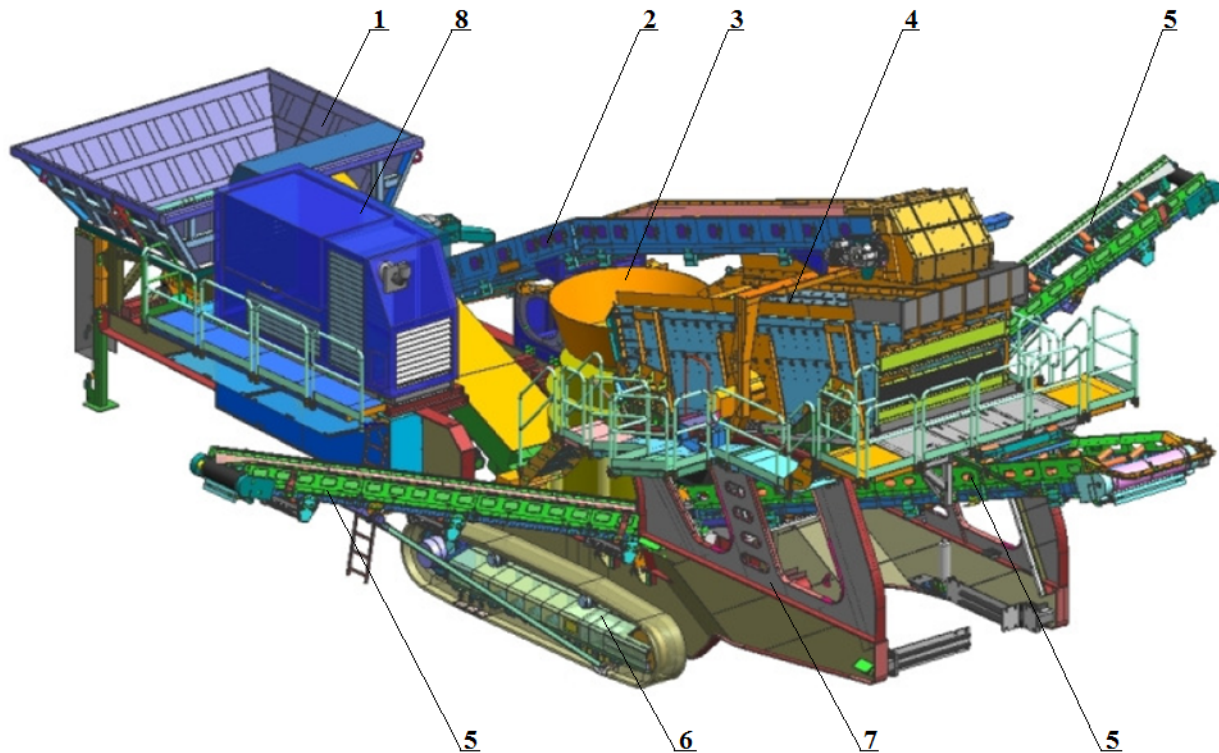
Загальний вигляд пересувної дробильно – сортувальної установки, виготовленої на базі конусної дробарки і вібраційного грохота
